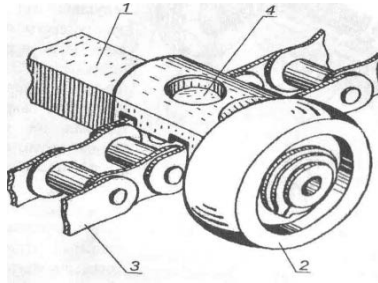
Механизм прессующий: 1 – планка (скалка); 2 – роликовая опора; 3 – цепь; 4 – фиксатор
